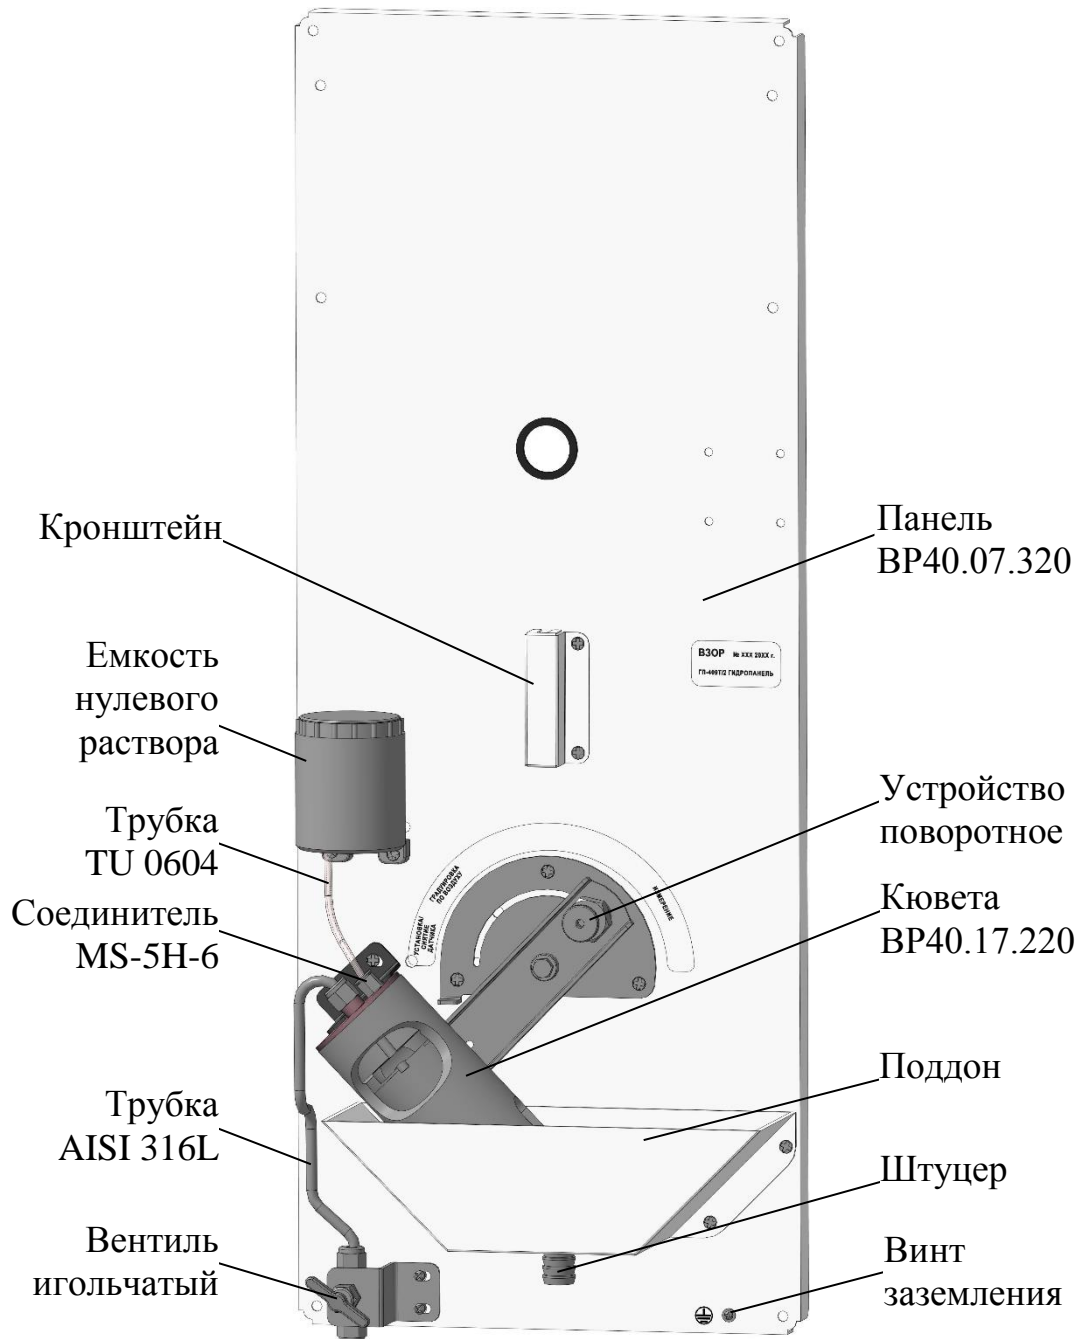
Гидропанель ГП-409Т/2 (вид с местным разрезом)
